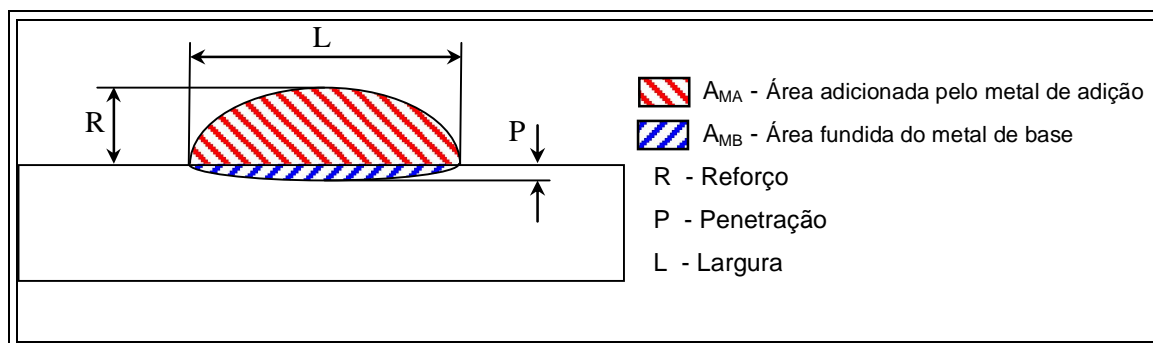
Desenho esquemático das características geométricas e diluição para um cordão de solda.
